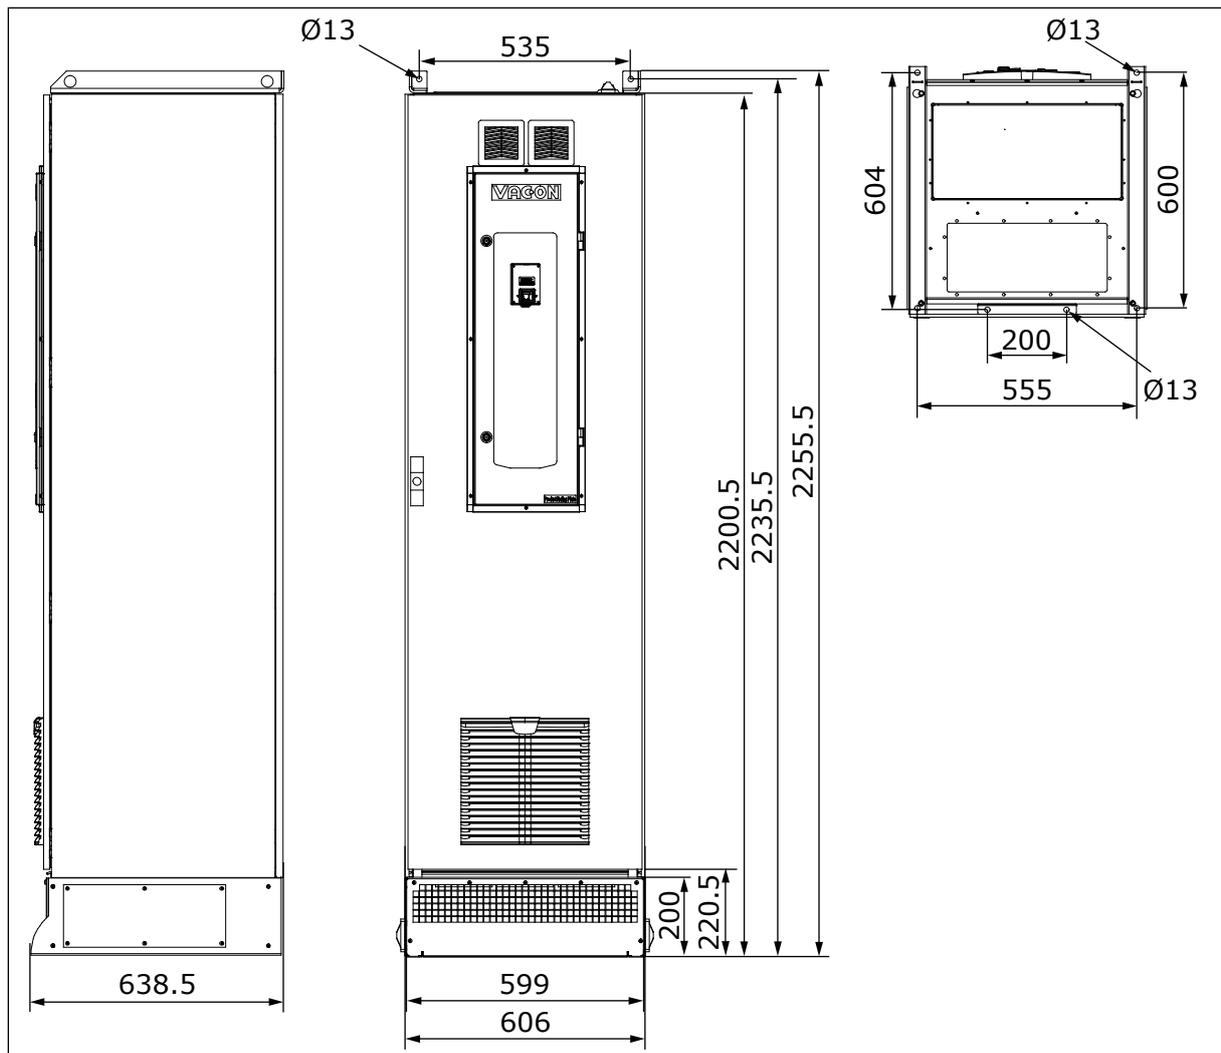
Abmessungen des Standard-Schaltschranks in mm, MR9 und MR10, NAM
